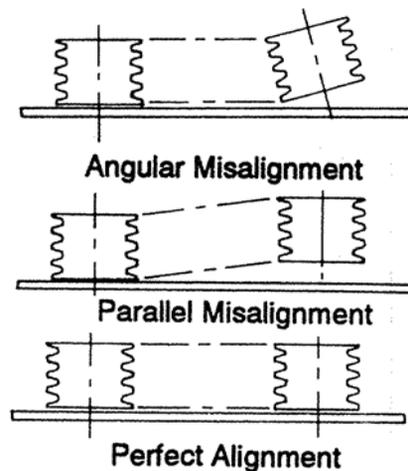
Entraînement par courroie trapézoïdale – Alignement
